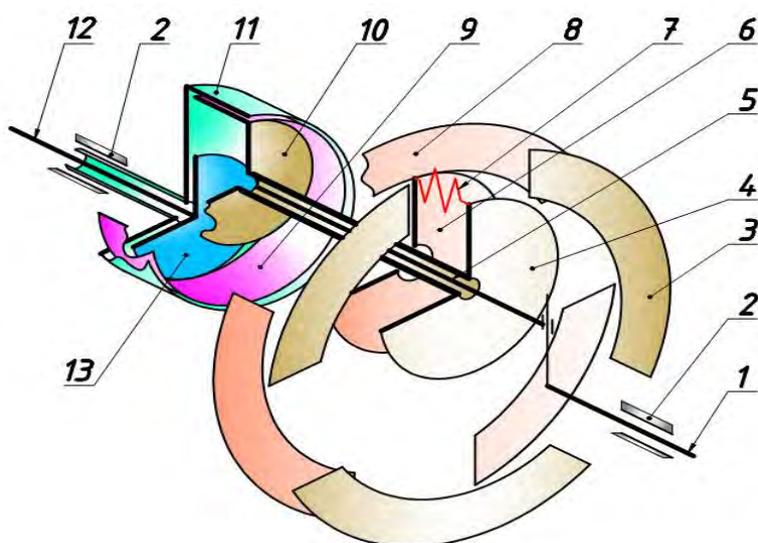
Схема зубчатой планетарной плавнорегулируемой передачи: 1 – ведущий вал; 2 – корпус; 3 – зубчатый сектор первого силового потока центрального зубчатого колеса; 4 – зубчатый венец первого силового потока сателлита; 5 – водило; 6 – зубчатый венец второго силового потока сателлита; 7 – упругая связь; 8 – зубчатый сектор второго силового потока центрального зубчатого колеса; 9 – зубчатое колесо с внутренними зубьями вспомогательной планетарной передачи для съема вращения с сателлита; 10 – вспомогательный зубчатый венец сателлита-сателлит вспомогательной зубчатой передачи; 11 – обойма для поддержания зубчатого колеса с внутренними зубьями вспомогательной планетарной передачи; 12 – выходной вал; 13 – зубчатый венец выходного вала
